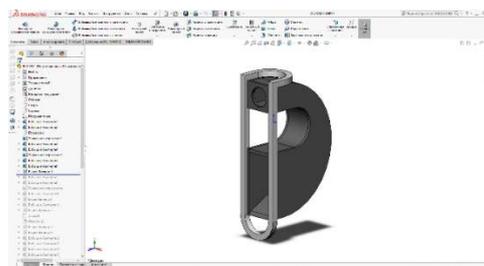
Трехмерное эскизирование опорной стойки корпуса АС.
